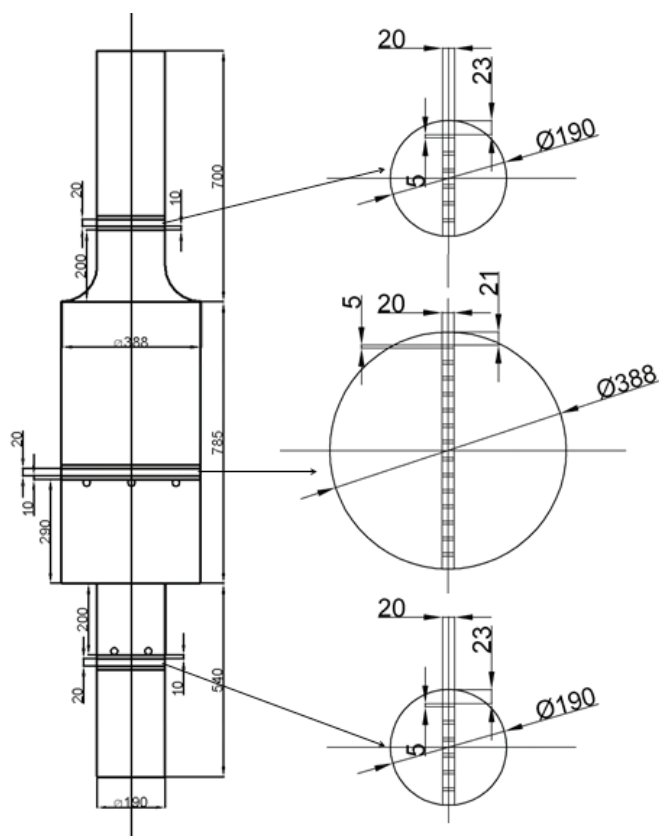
Схема разрезки и отбора образцов от серийного и опытного валков
